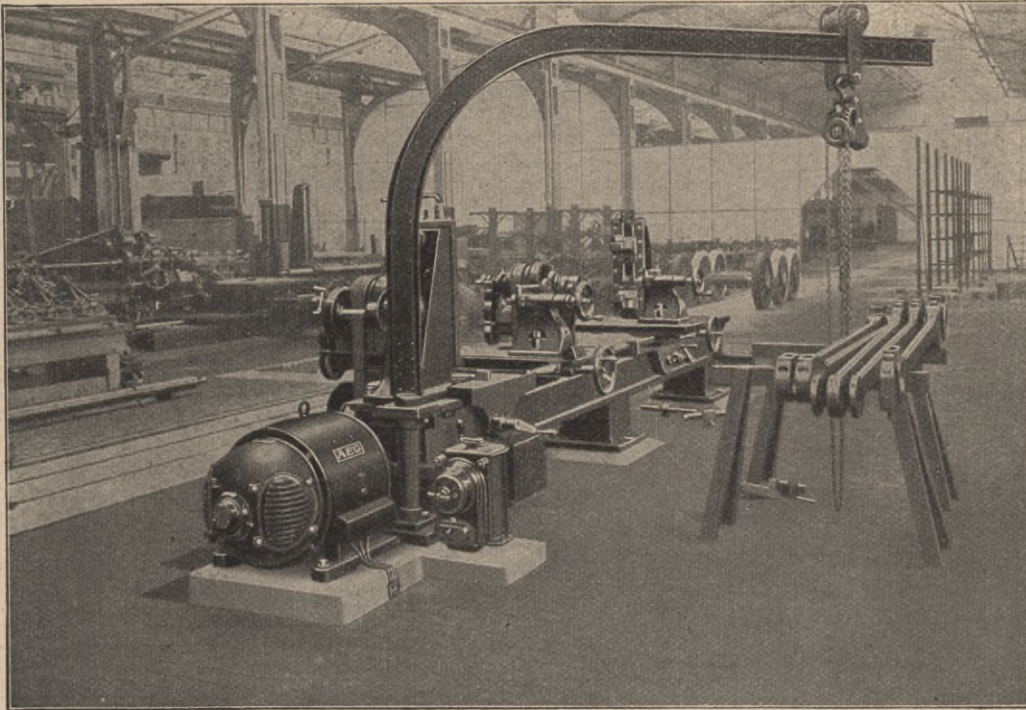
Doppel-Pleuelstangen-Fräsmaschine mit regelbarem Motor
